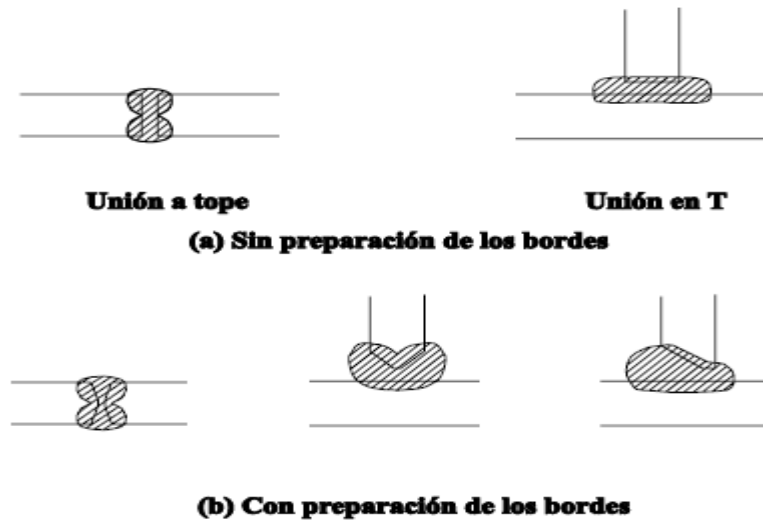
Soldaduras con y sin preparación de bordes
